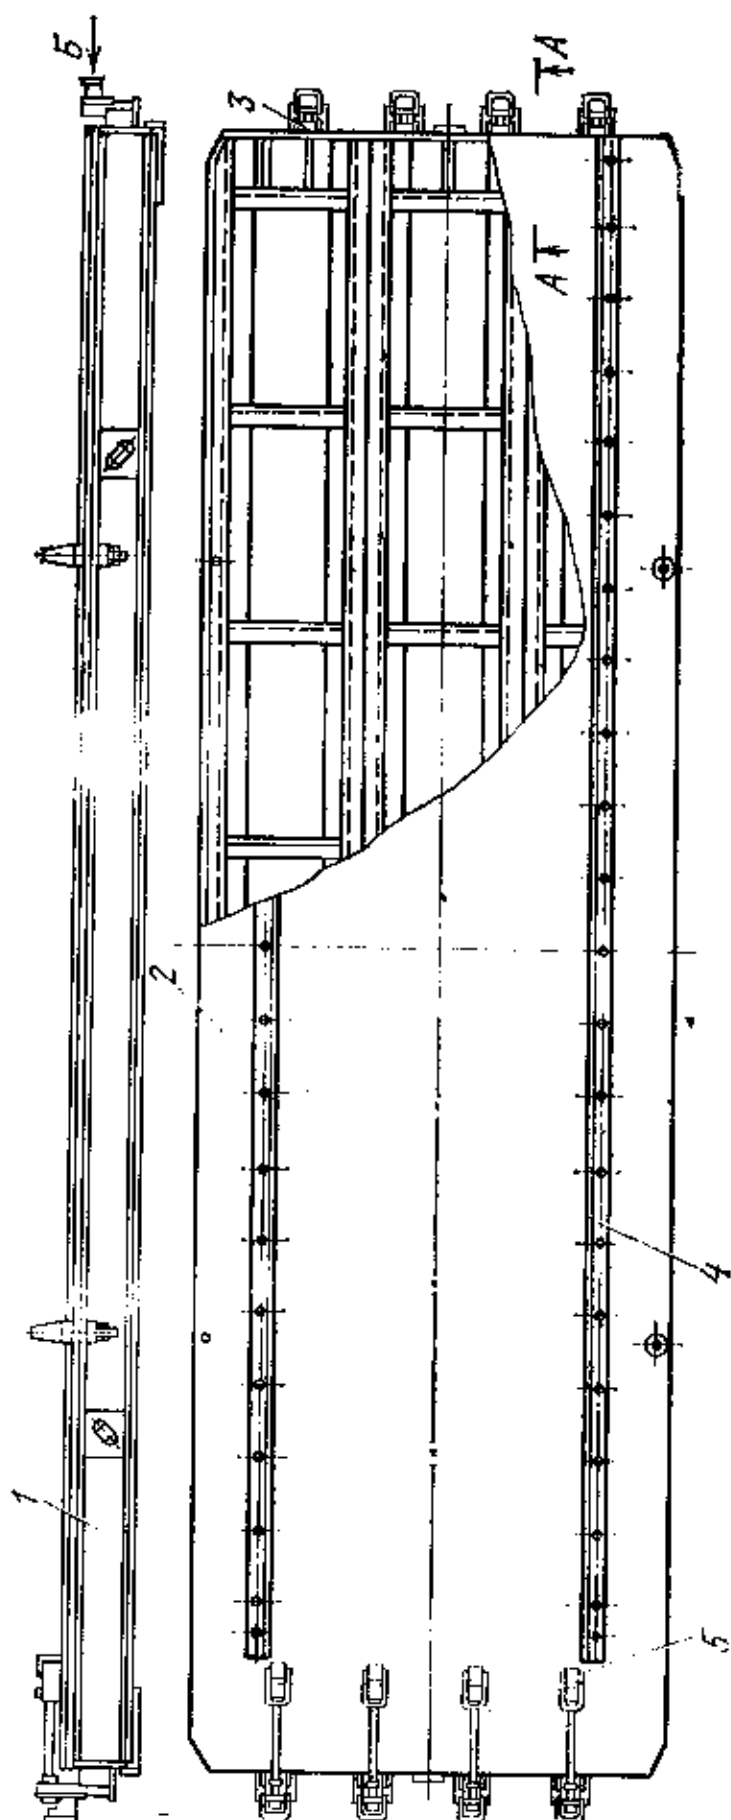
Поддон СМЖ-548 для изготовления многопустотных панелей перекрытий
